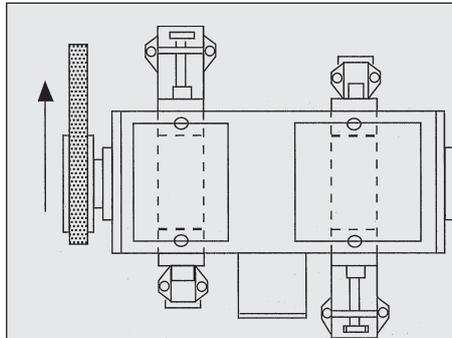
Disposición de la guía de deslizamiento y el tornillo de tensión.
